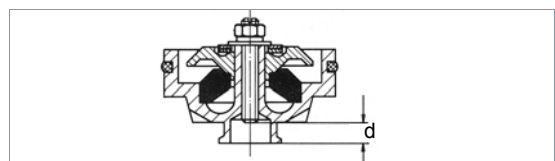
Maß d (Gerät mit einer Gummifeder)
